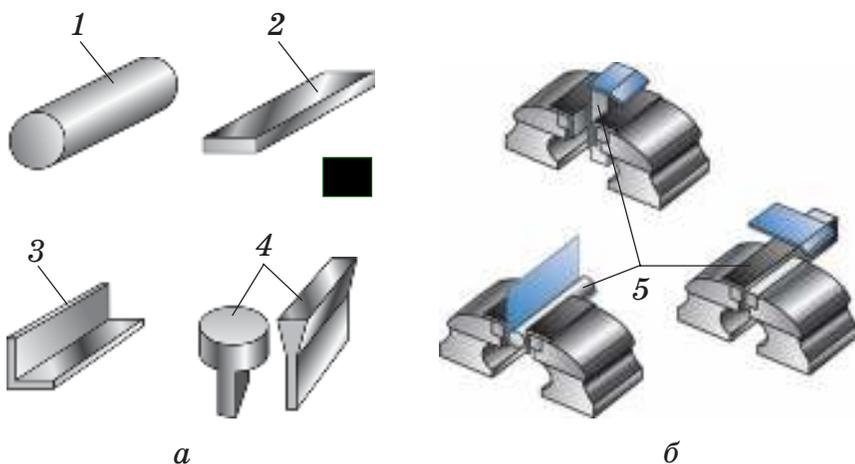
Гибка тонколистового металла с применением оправок: а — виды оправок: 1 — цилиндрическая, 2 — прямоугольная, 3 — уголковая, 4 — фигурные; б — установка оправок в тисках: 5 — оправки
